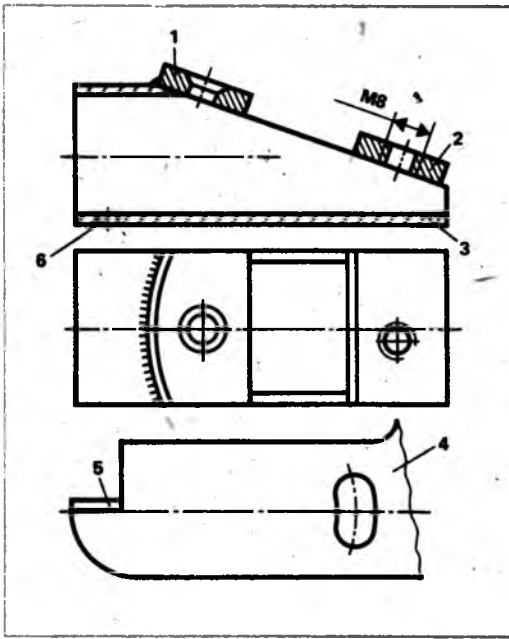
Устройство для крепления ножа и регулирования захвата косы: 1, 2 — пластины; 3 — труба; 4 — пятка ножа косы; 5 — шпик пятки; 6 — отверстие для шурупа
